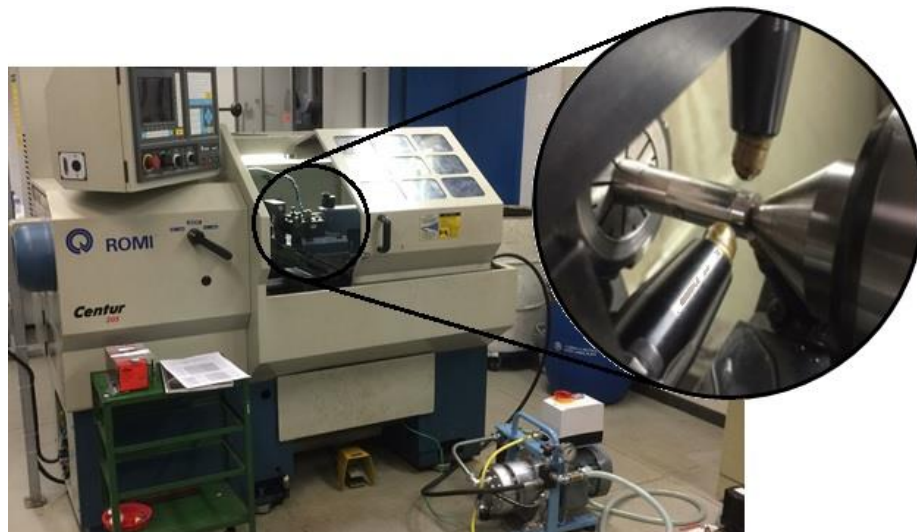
Montagem da ferramenta de roleteamento e do seu sistema de pressurização junto ao torno CNC para realização dos ensaios de roleteamento dos corpos de prova.
